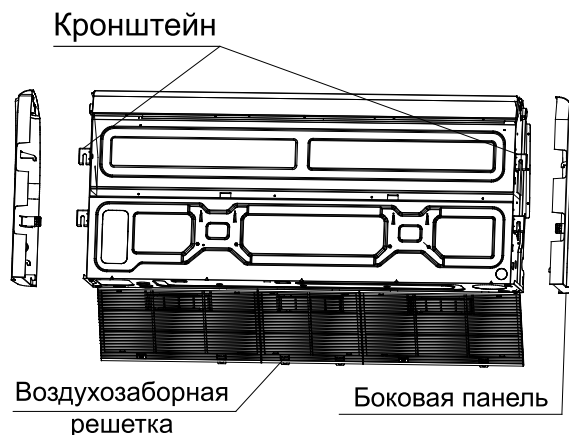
Подготовка к монтажу внутреннего блока напольно-потолочного типа
